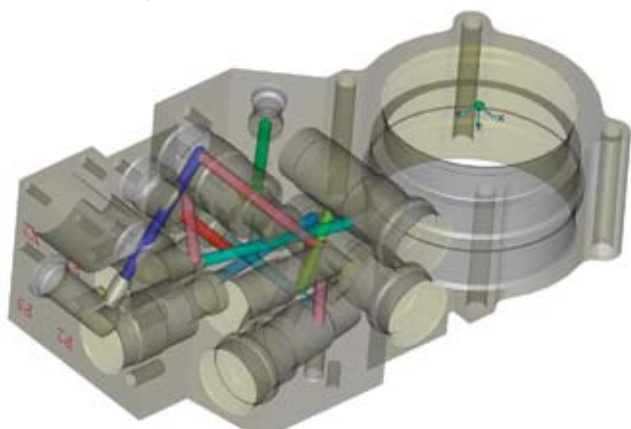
Модель для многопозиционной фрезерной и сверлильно-расточной обработки
